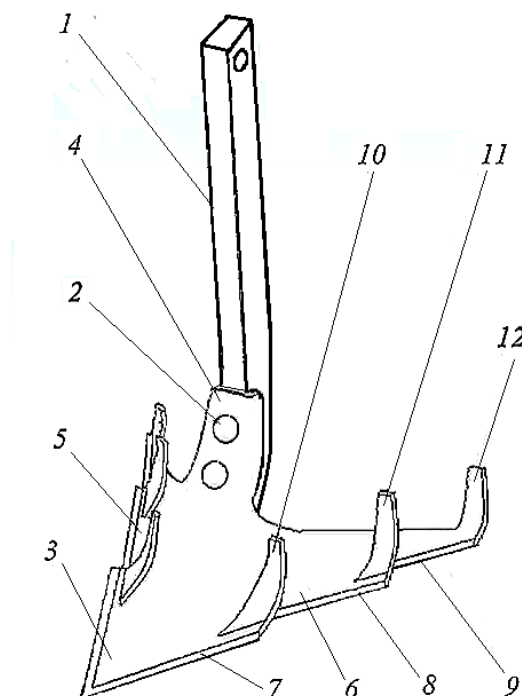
Пассивный рабочий, снабженный ступенчатой лапой
